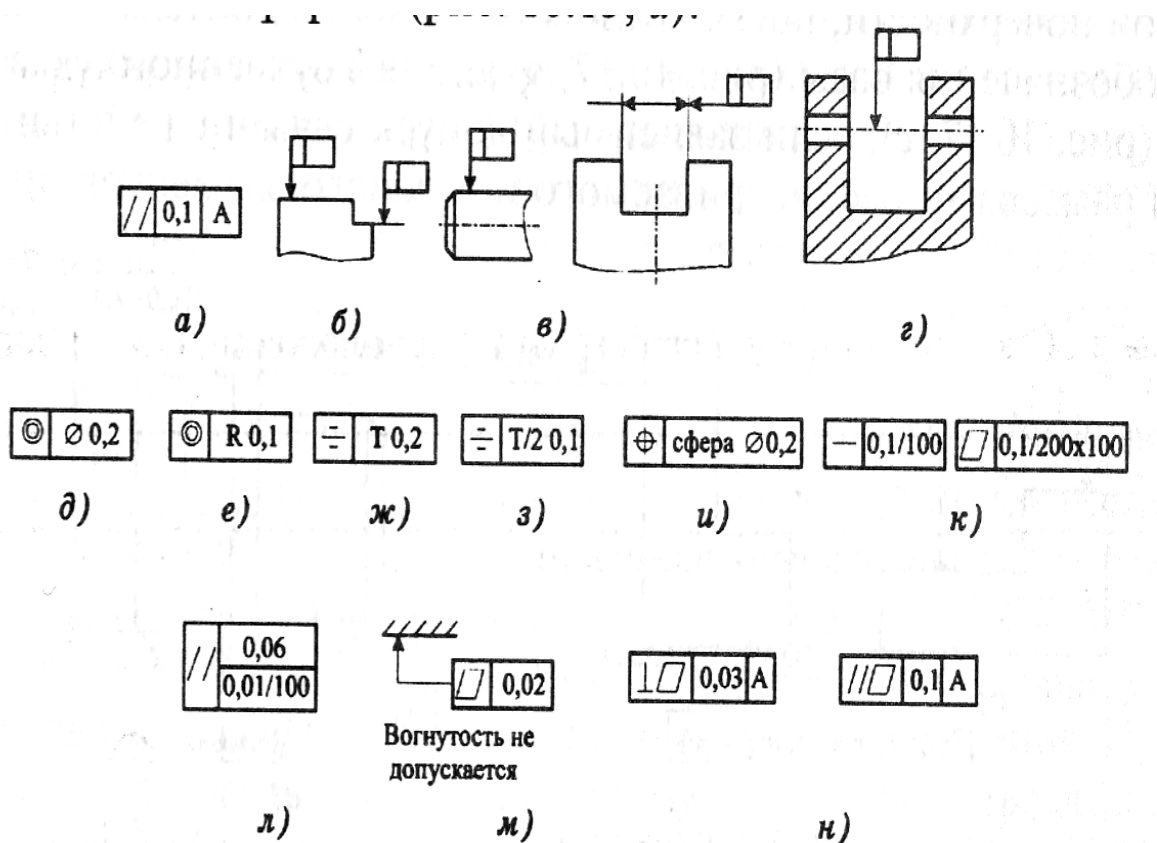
Схема указания допусков формы и расположения поверхностей
